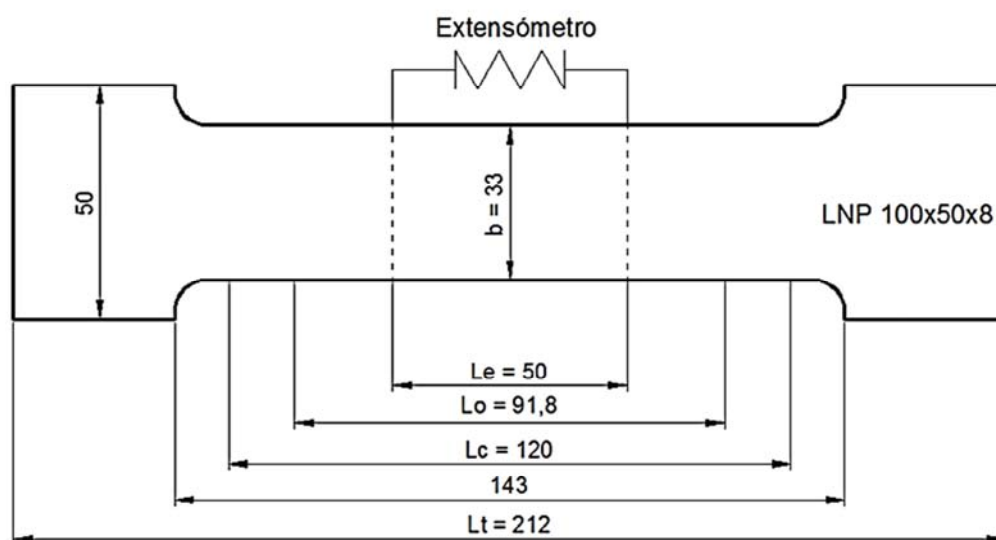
Dimensões dos provetes maquinados para secções de espessura 8 [mm].
